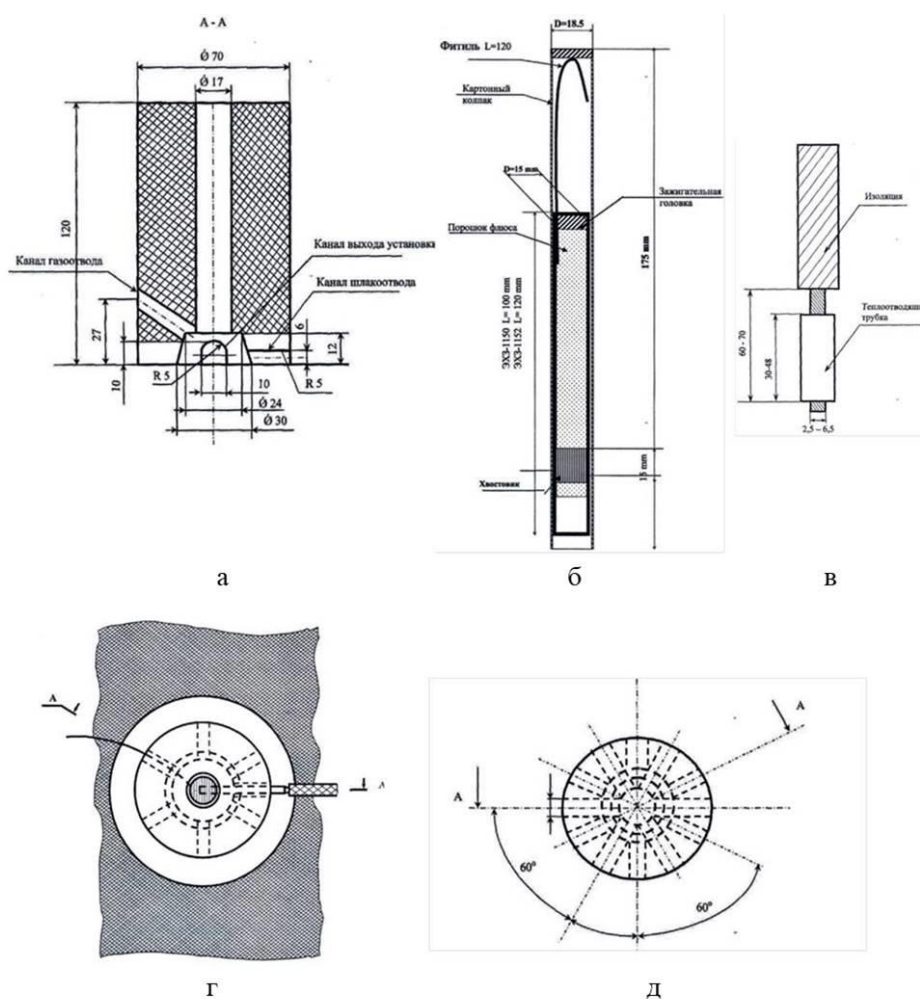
Конструктивные размеры графитовой оправки и паяльно-сварочного стержня
